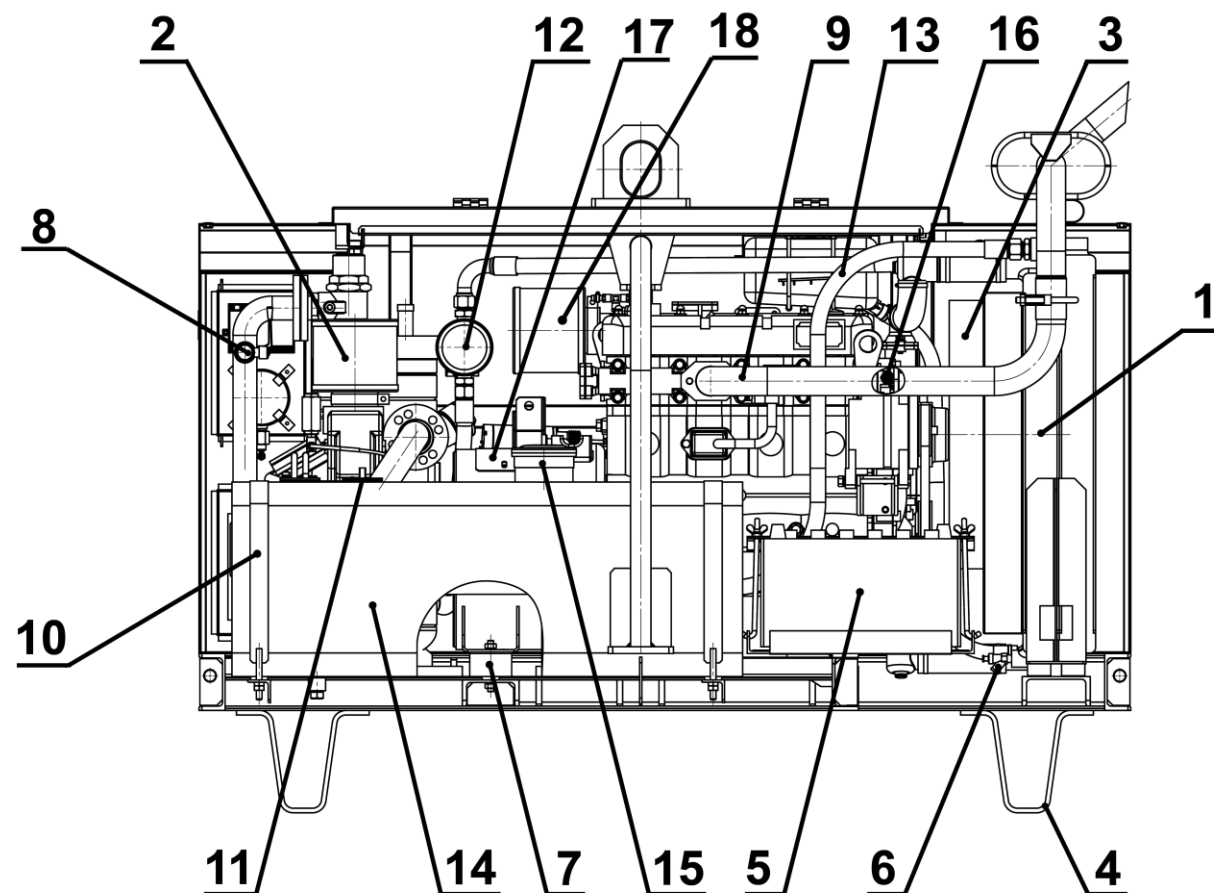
Габаритный чертеж станции компрессорной ЗИФ-ПВ3,5/0,7Е (АРМ9-33)
